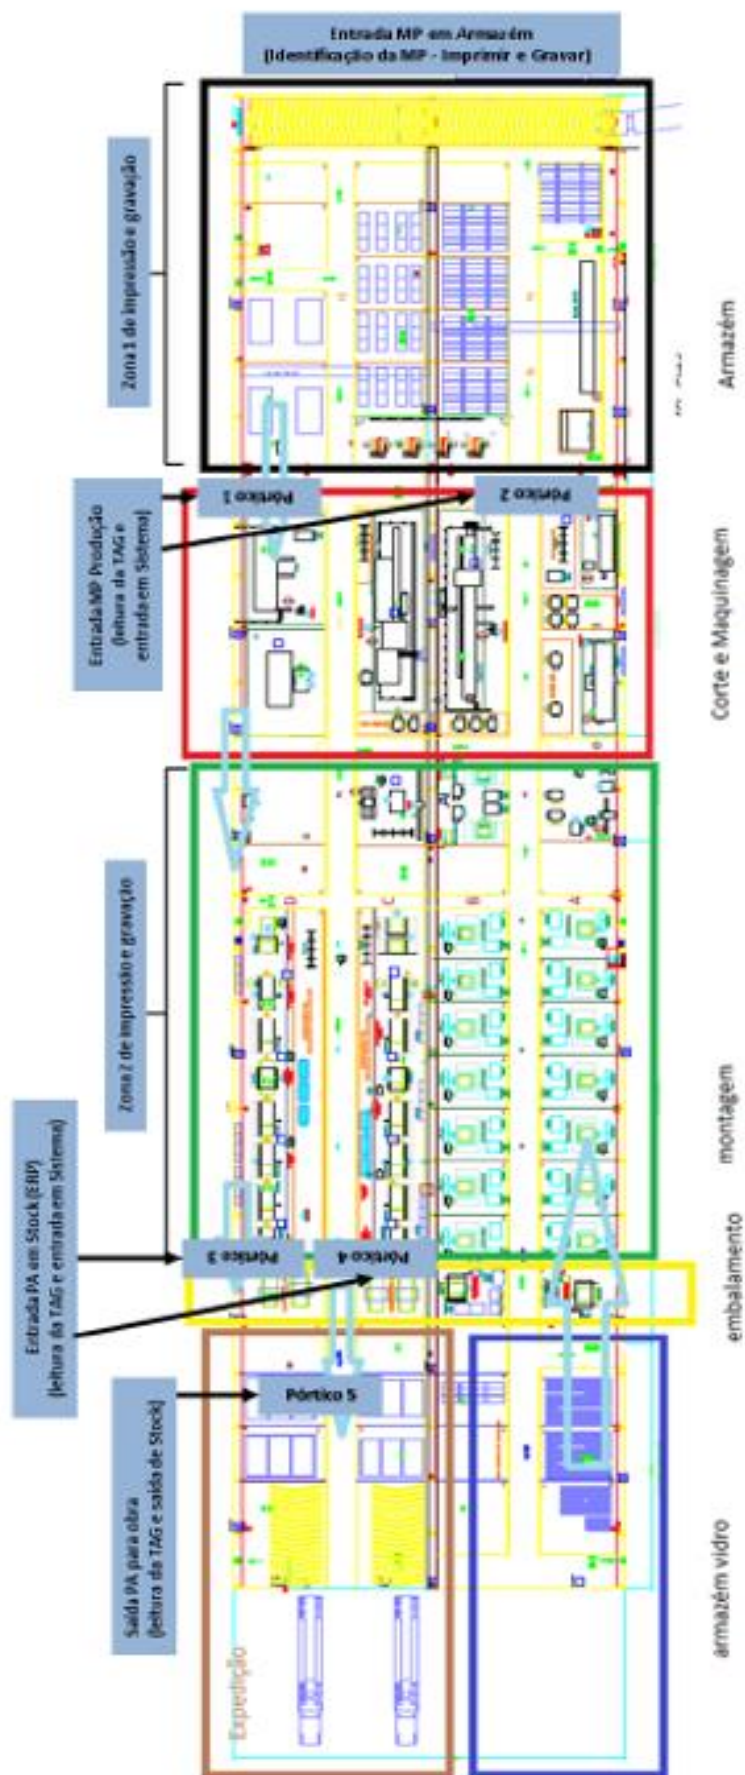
Projeto piloto armazém Bysteel FS - Bysteel
